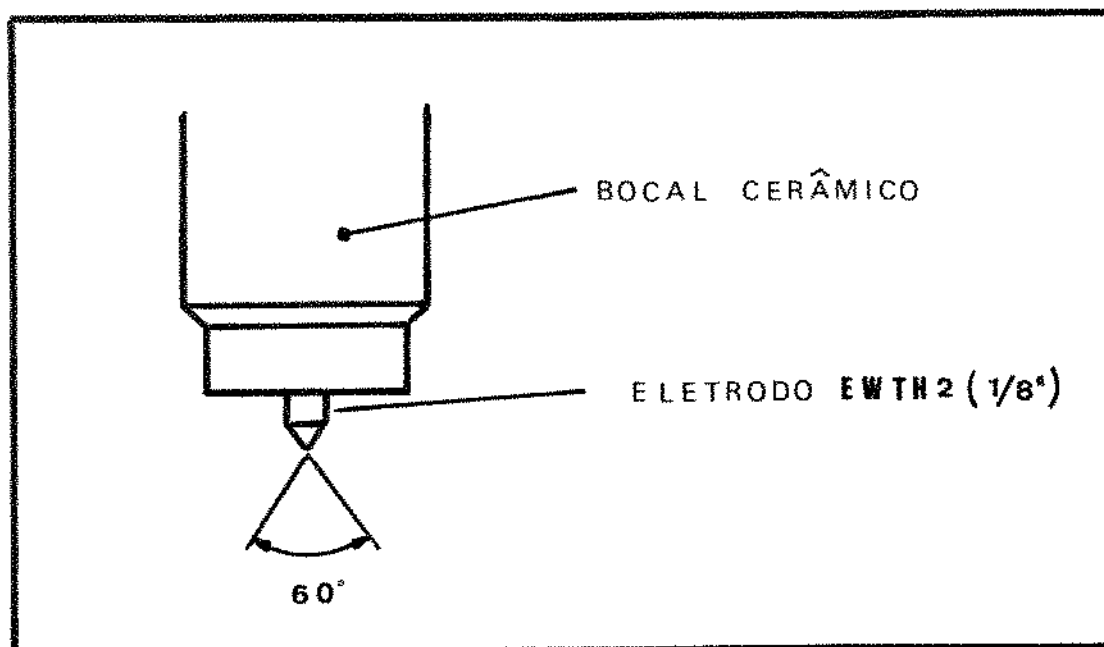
Detalhe do conjunto bocal/eletrodo [33 , 34]
